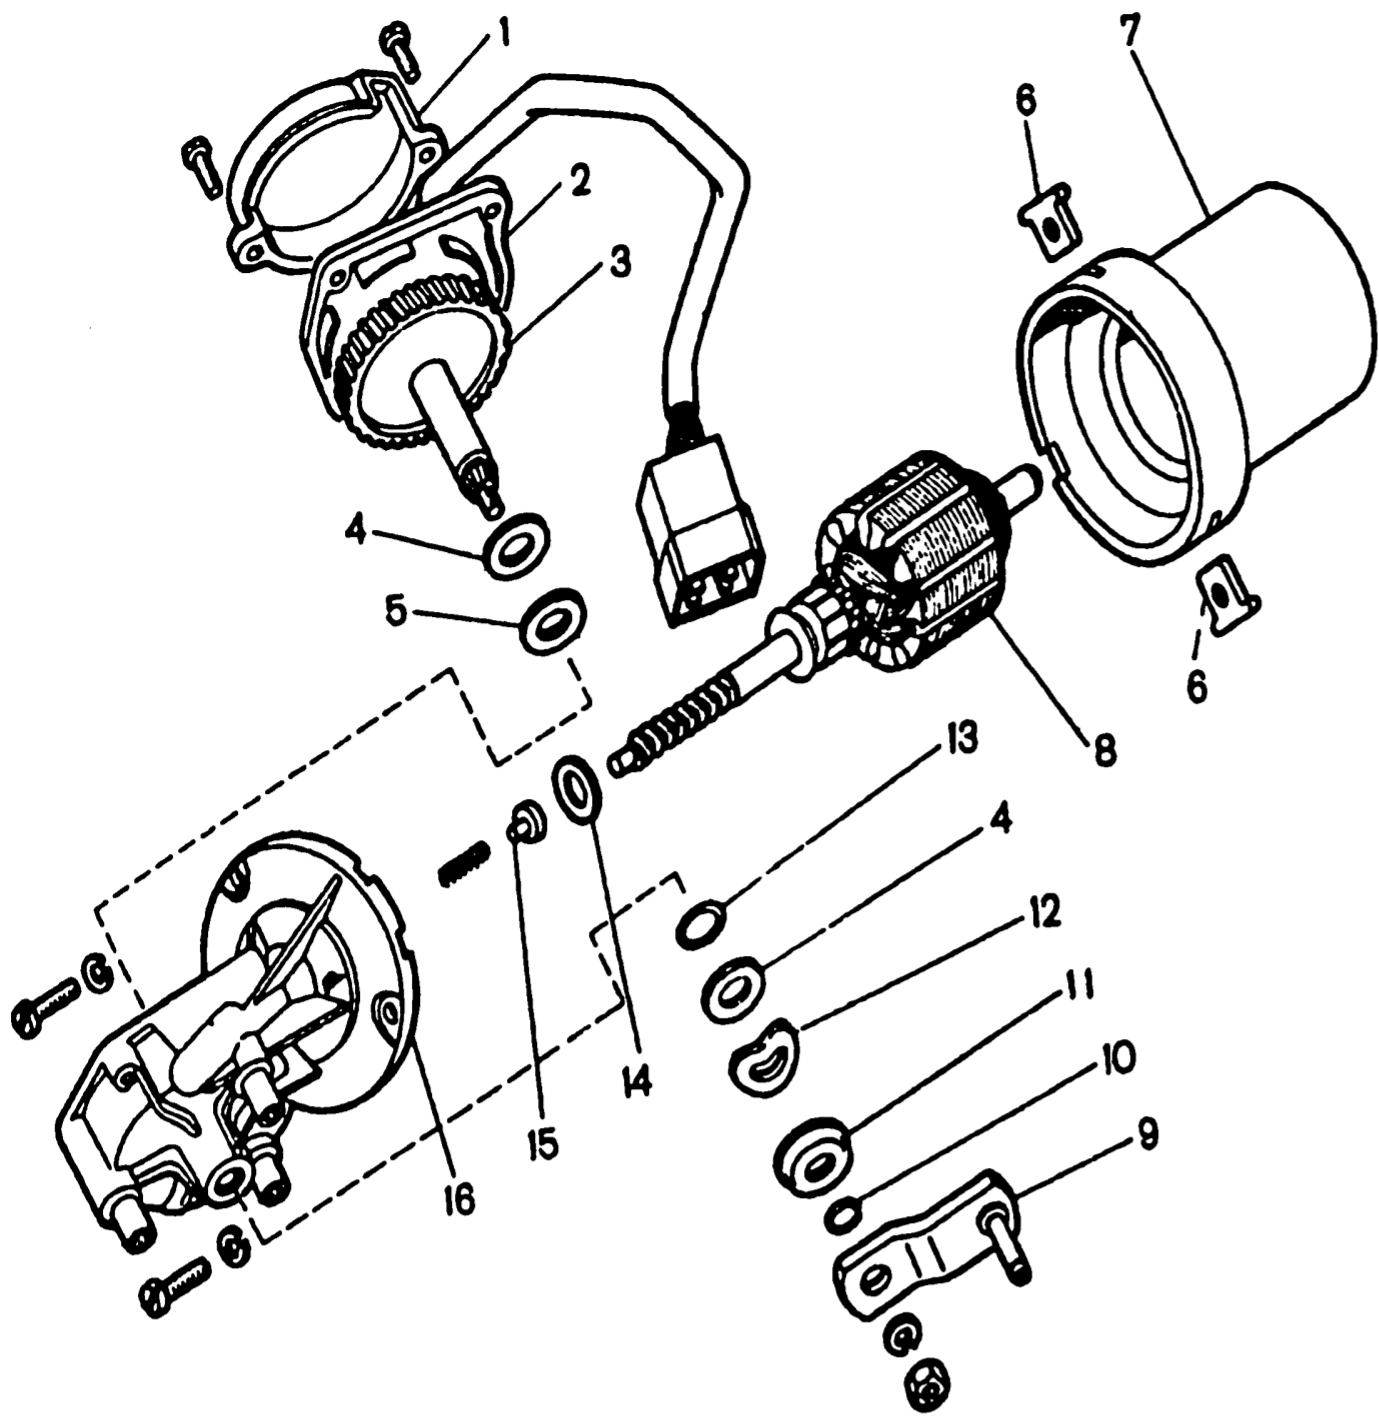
Детали электродвигателя стеклоочистителя: 1 - крышка; 2 - панель; 3 - шестерня редуктора; 4 - стальная шайба; 5 - текстолитовая шайба; 6 - сухарь; 7 - корпус; 8 - якорь; 9 - кривошип; 10 - стопорное кольцо; 11 - защитный колпачок; 12 - пружинная шайба; 13 - уплотнительное кольцо; 14 - регулировочная шайба; 15 - подпятник; 16 - крышка электродвигателя
